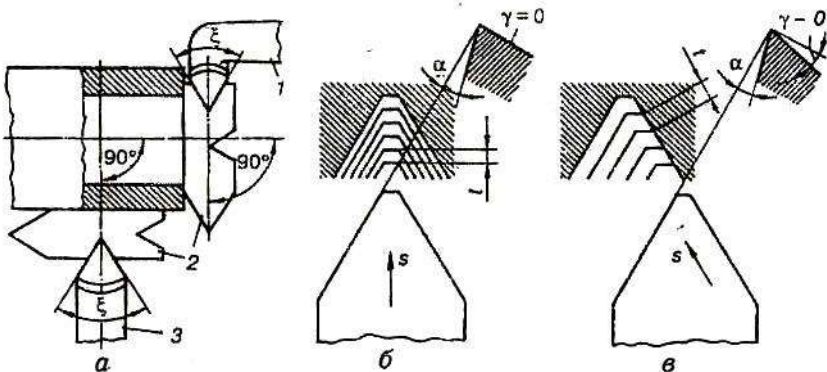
Схеми нарізання різьби на токарному верстаті
